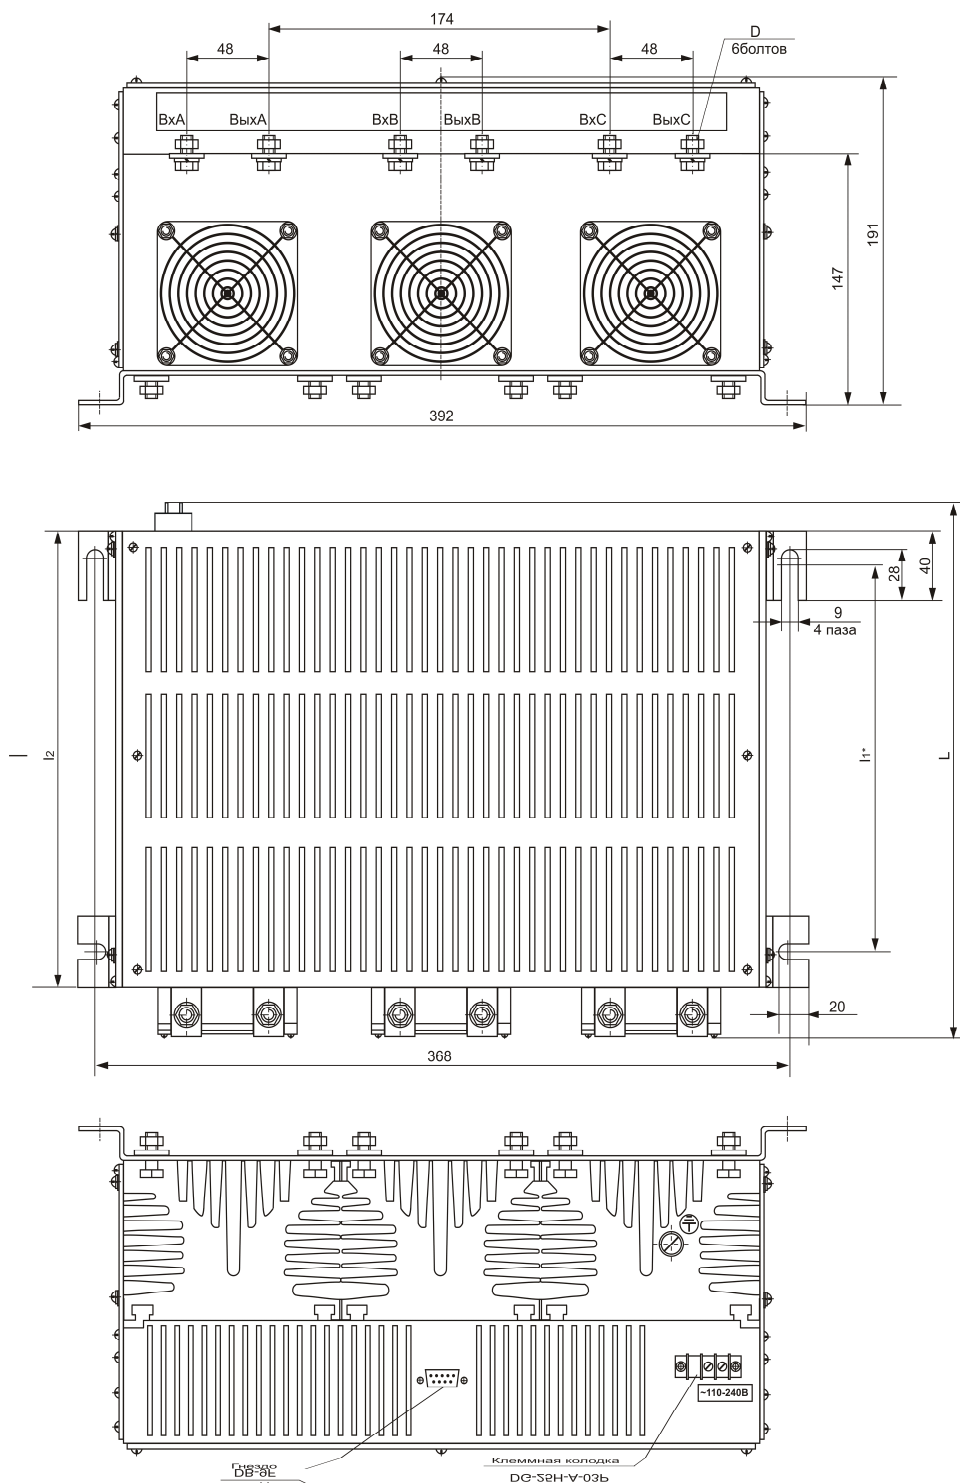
Габаритные и присоединительные размеры ТРМЗ
